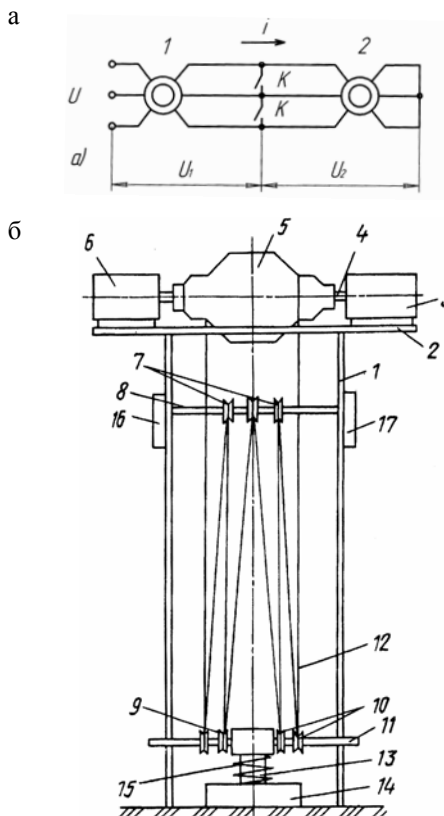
Схема соединения статорных обмоток двигателей (а) и конструктивная схема (б) станка качалки
